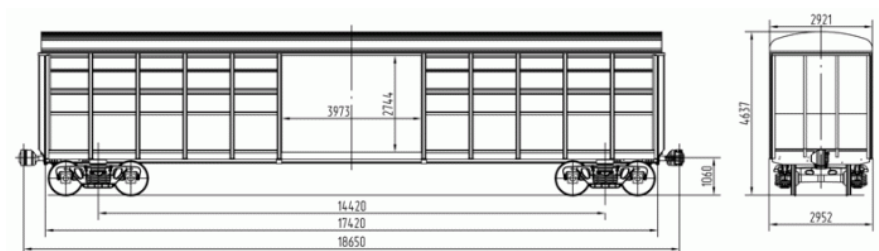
Внешний вид и размеры крытого вагона универсального
